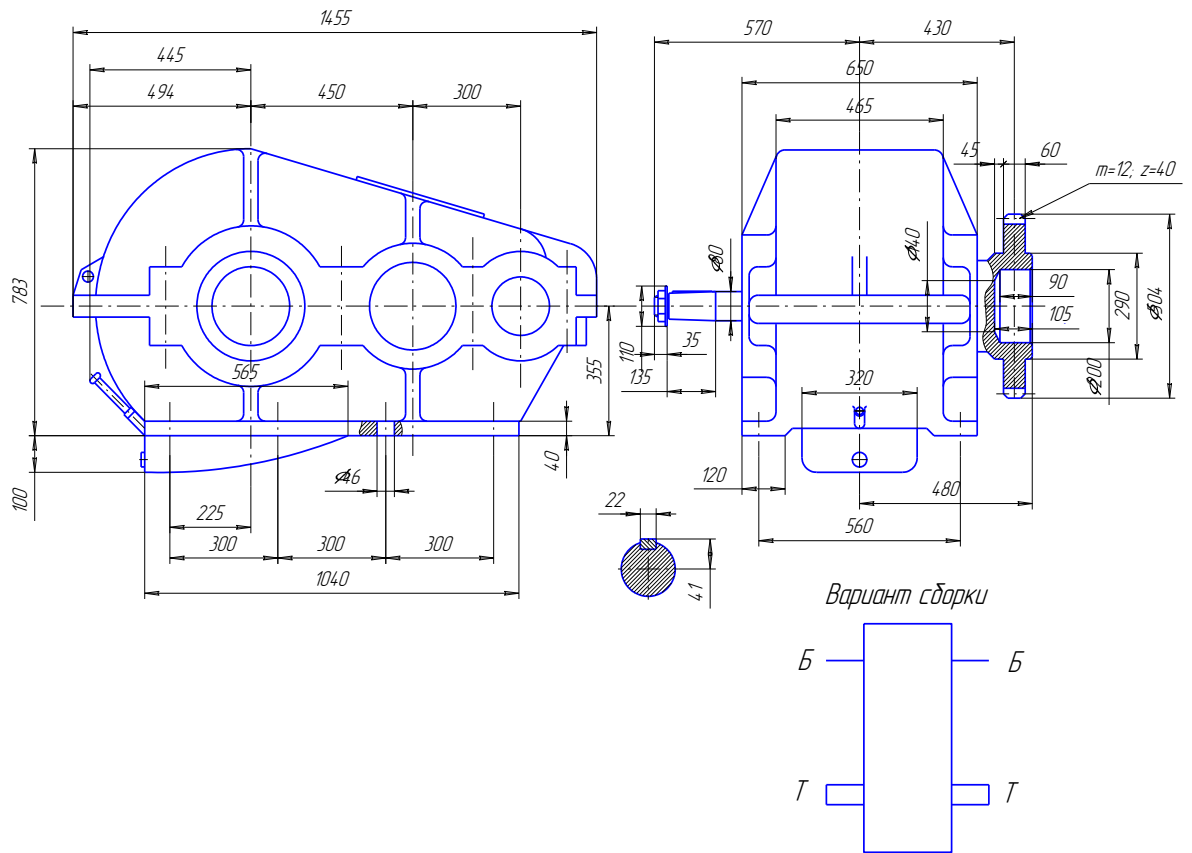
Габаритне креслення редуктора Ц2-650
